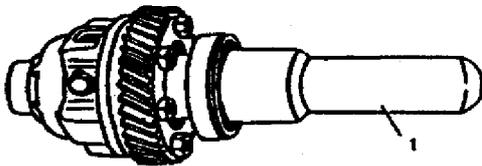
Instalação do rolamento: 1 - ferramenta 67.7853-9558
